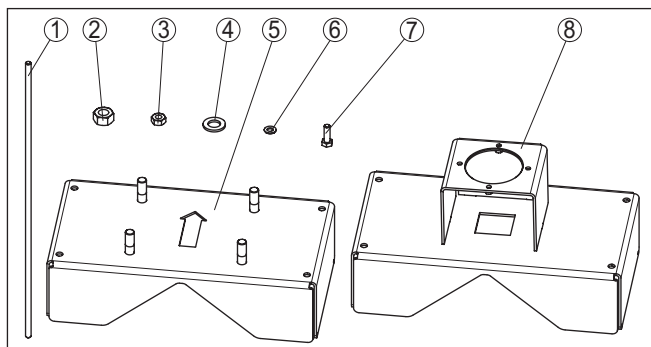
Dispositif de fixation pour conduites traversées perpendiculairement KV 31, Montage horizontal du capteur
